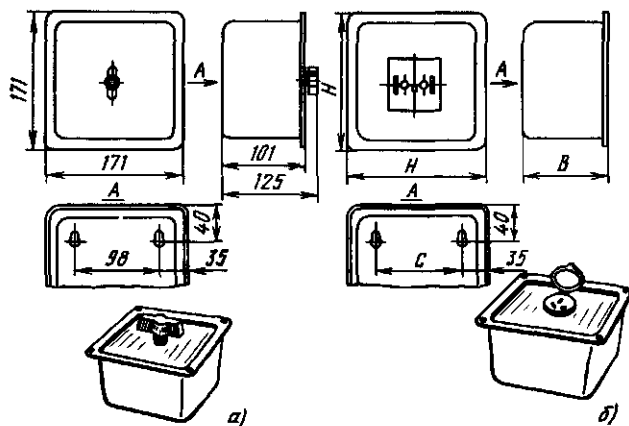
Коробки с выключателями КВ и розетками КР
